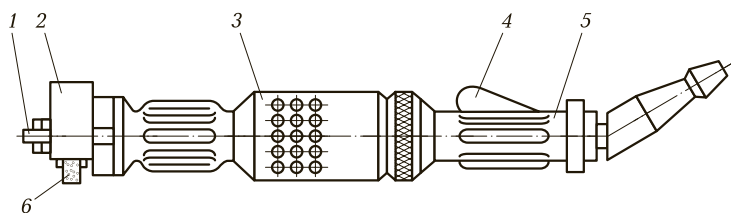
Пневматическая ручная шлифовальная машина:
